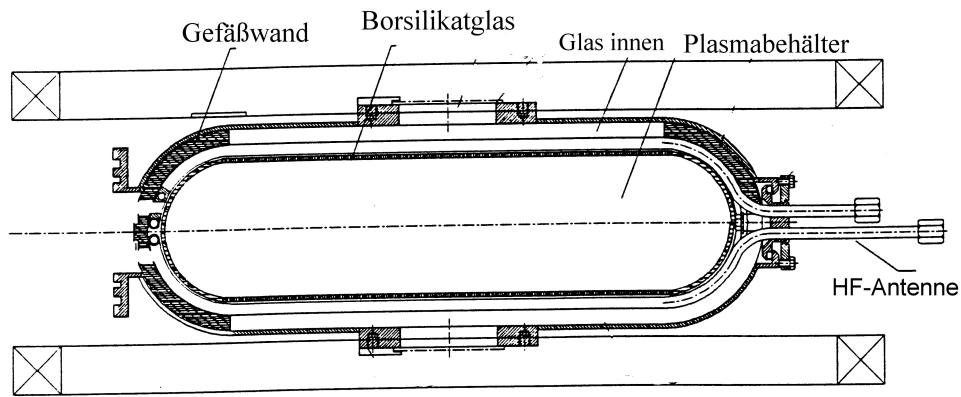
Draufsicht auf die ECWR-Quelle HQ/E-100 UHV.
